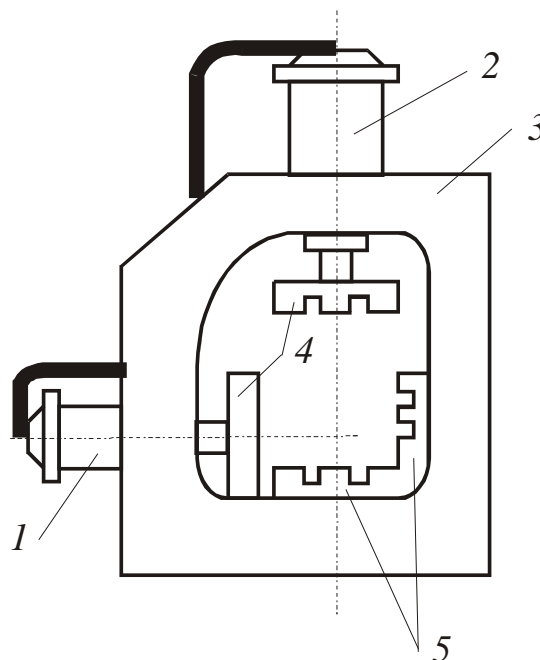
Угловой пресс с одним угловым цилиндром:
